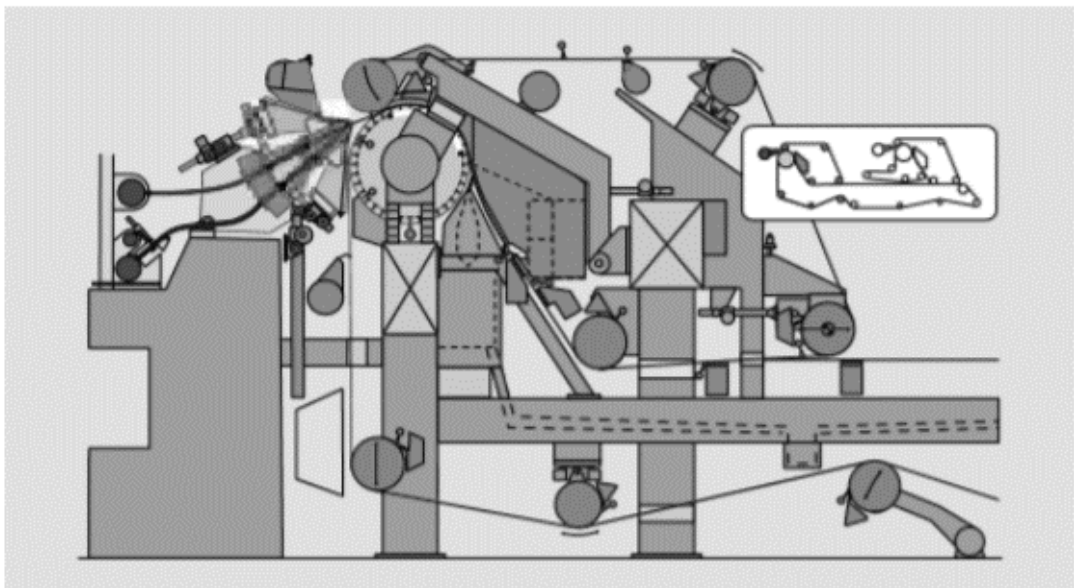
Формуючий пристрій DuoFormer™ Base з прикладом встановлення додаткового формера DuoFormer™ Top
